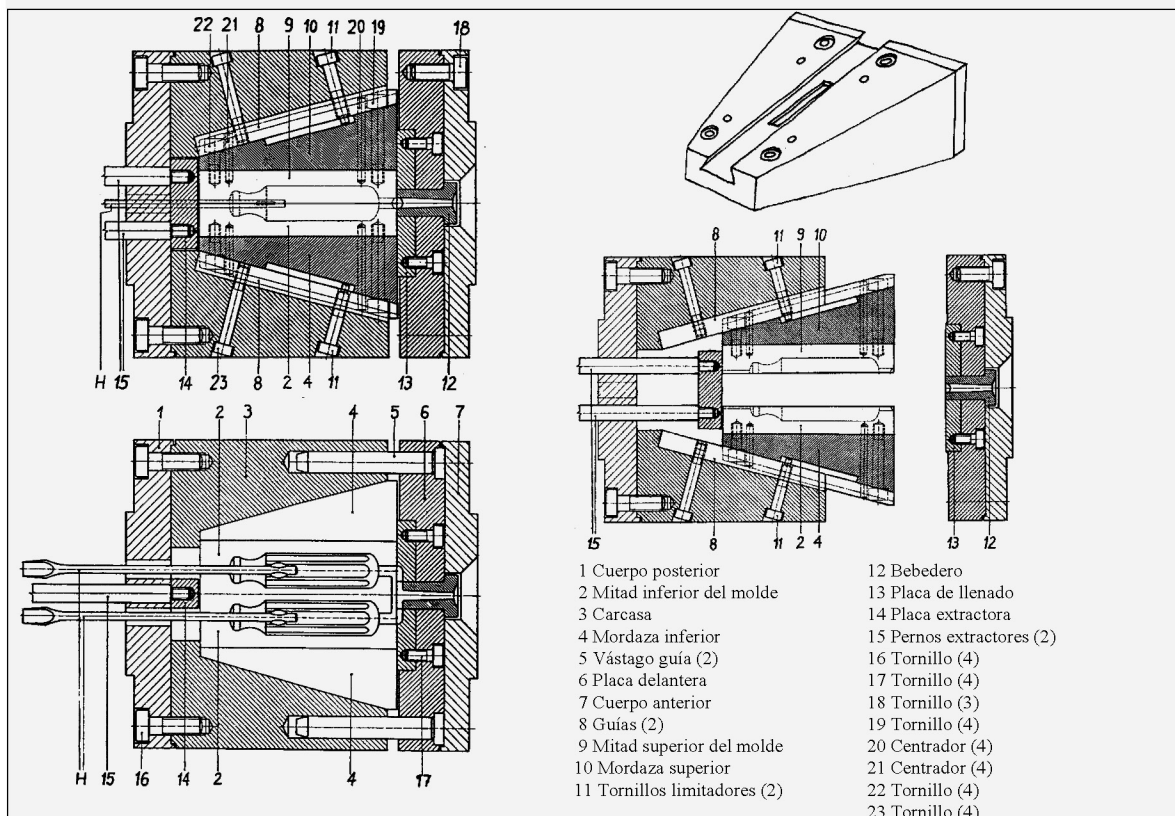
Molde para mangos de destornillador en su posición de cerrado (izquierda) y durante el proceso de apertura (derecha)
